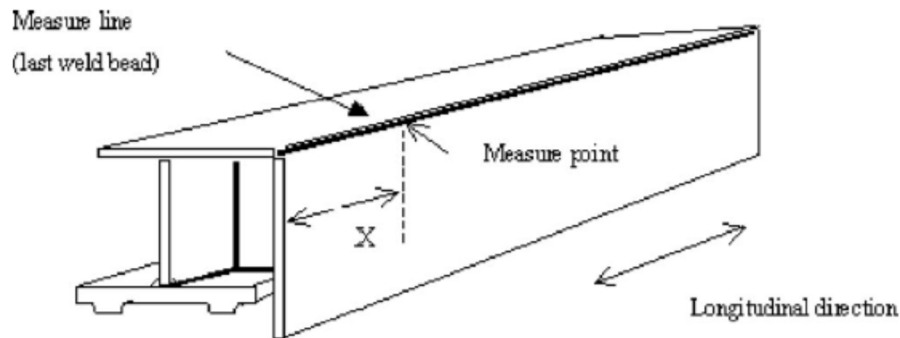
Werkstück mit Schweissnähten (aus [60])
